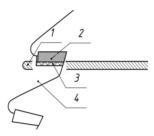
Расположение рабочей части индуктора относительно спаиваемых деталей: 1 – индуктор, 2 – напаиваемая твердосплавная пластина, 3 – припой, 4 – корпус инструмента
